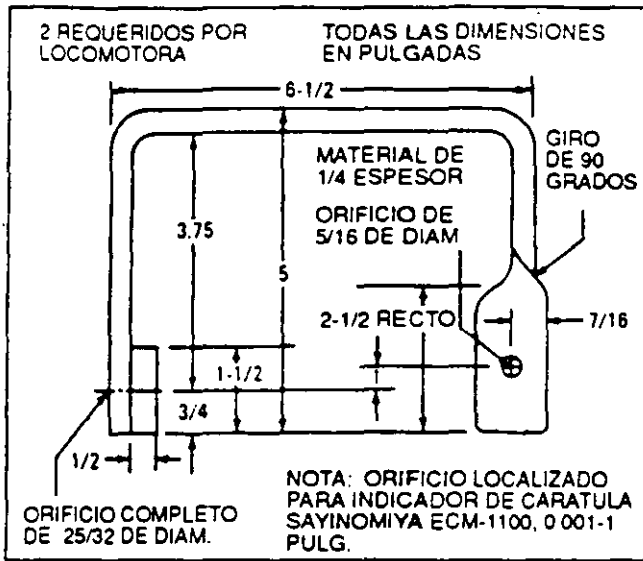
SOPORTE PARA EL INDICADOR DE CARATULA DE LA FLECHA IMPULSORA DEL COMPRESOR DEL LADO DEL COMPRESOR. (SOPORTE: PARTE GE 41D727866G1; SOPORTE E INDICADOR: PARTE GE 41D727866G5). E-31224B-S
